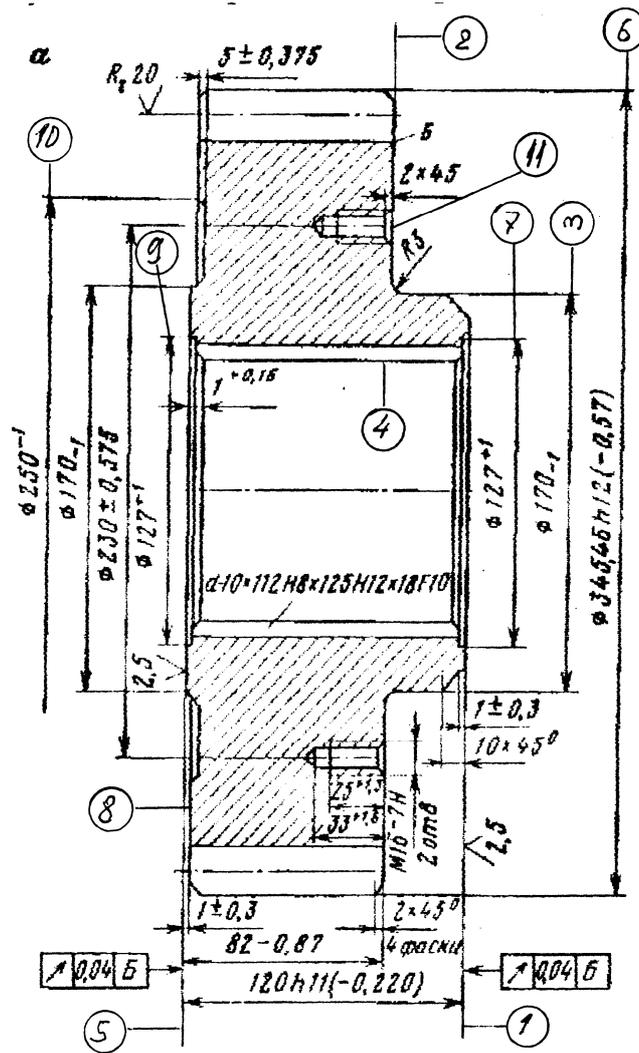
Зубчатое колесо редуктора очистного комбайна РКУ10
